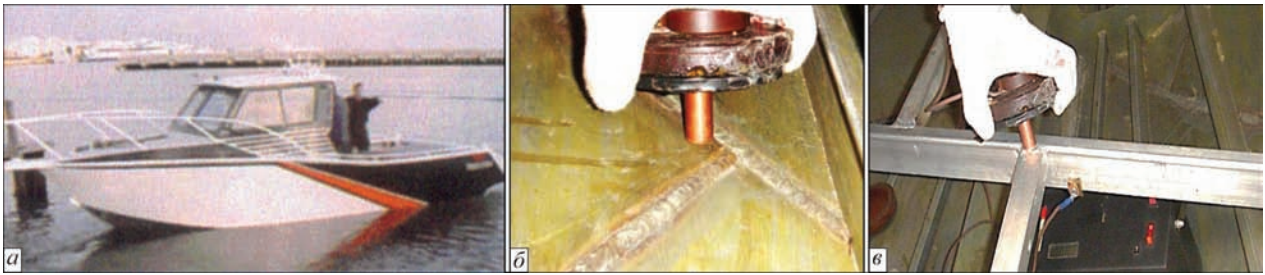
Применение ЭДО при изготовлении корпуса судна из сплава АМг6: а — внешний вид корпуса; б — ЭДО-правка сварных соединений обшивки; в — ЭДО-правка балочных конструкций днища
